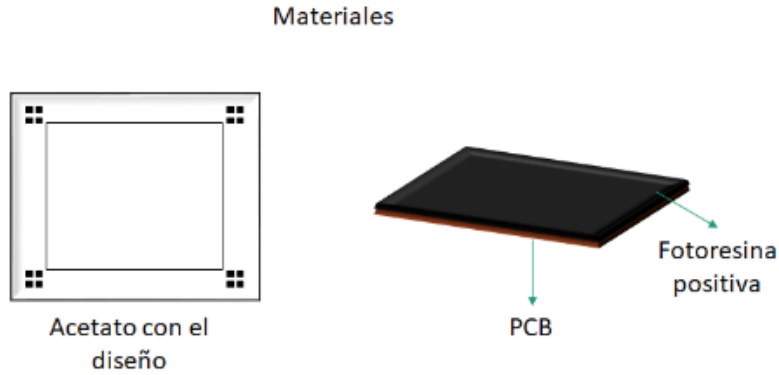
Materiales para utilizar en el diseño del PCB FR-4.
